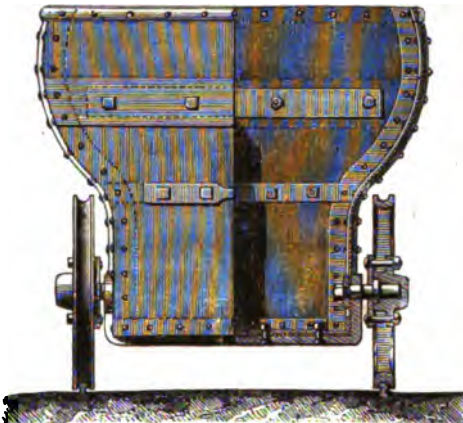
Waggon d'Anzin. Élévation et coupe transversale.
